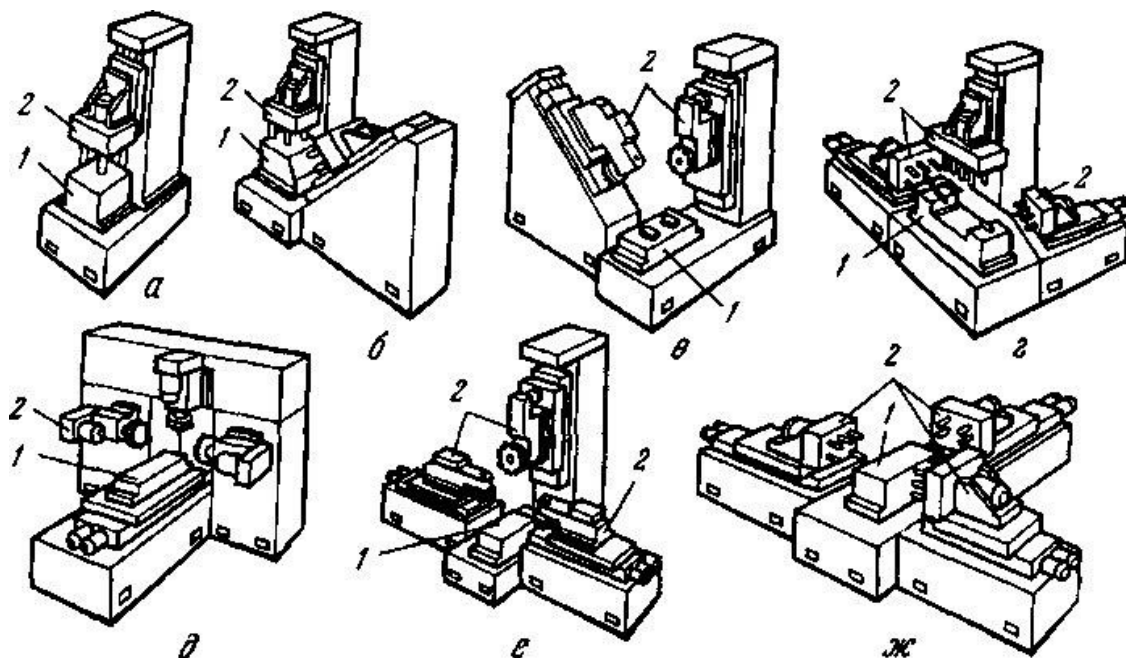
Типові компоновки агрегатних верстатів зі стаціонарними пристосуваннями
